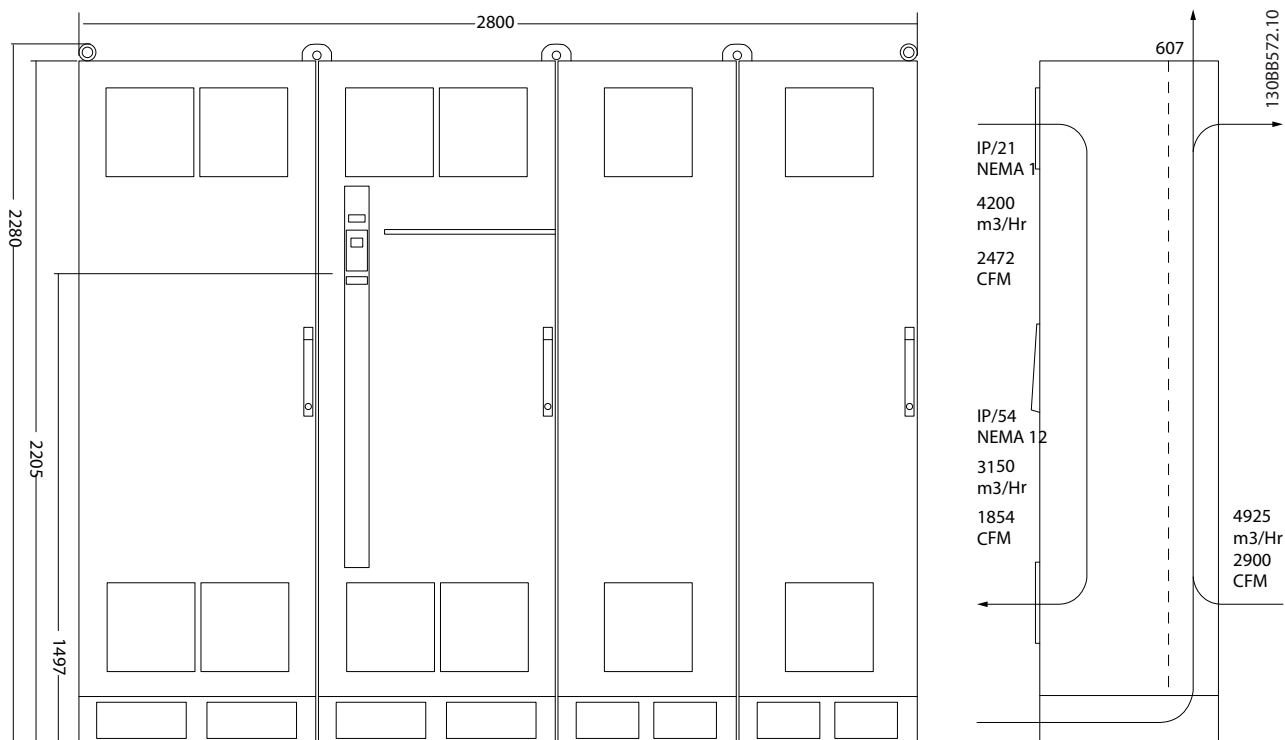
Dimensões Mecânicas (mm), F13
